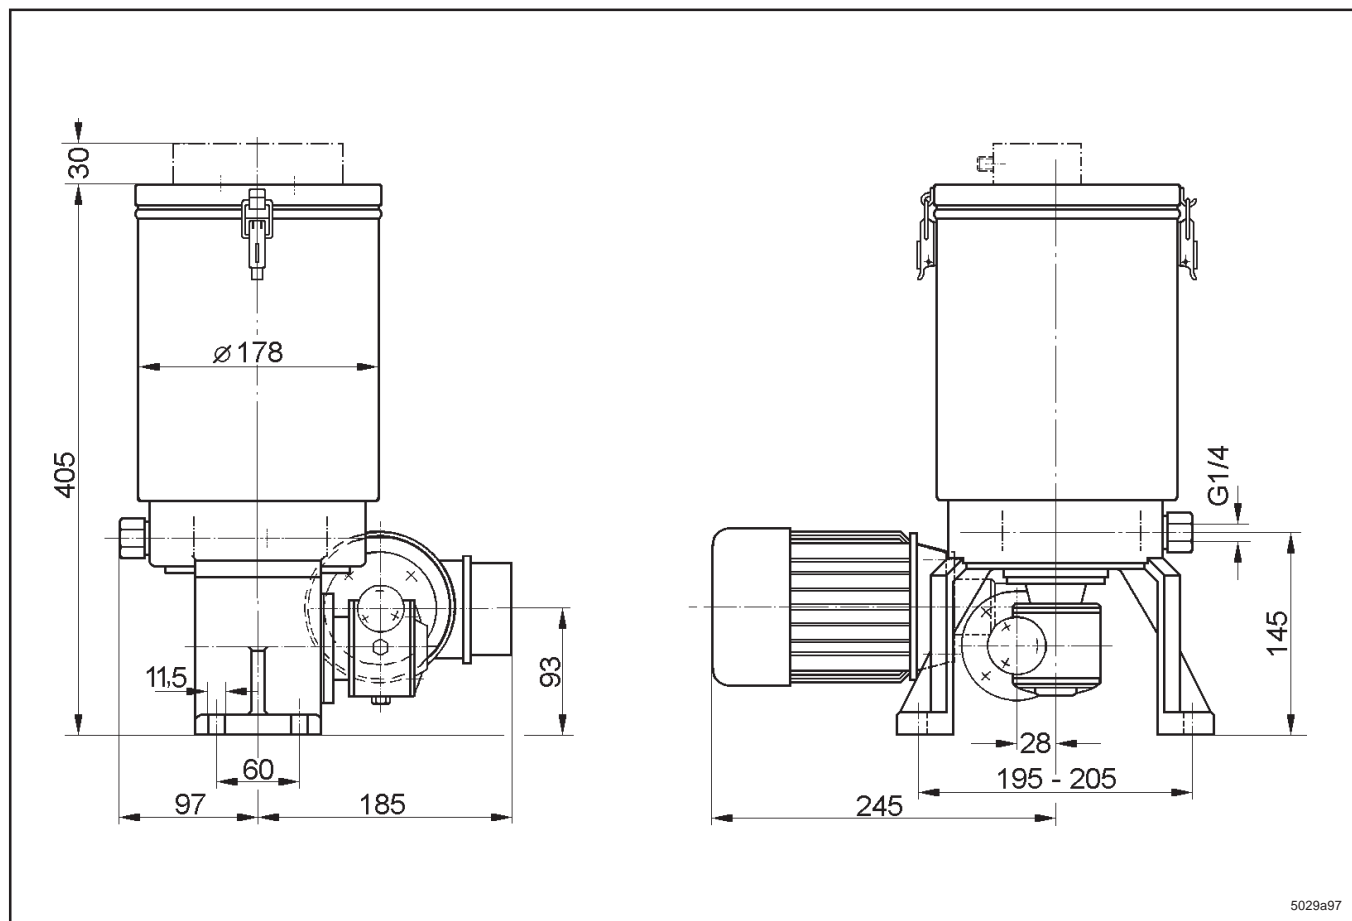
Maßzeichnung für Pumpe P205, 2-stufiges Getriebe, 5l Blechbehälter, Motorantrieb
